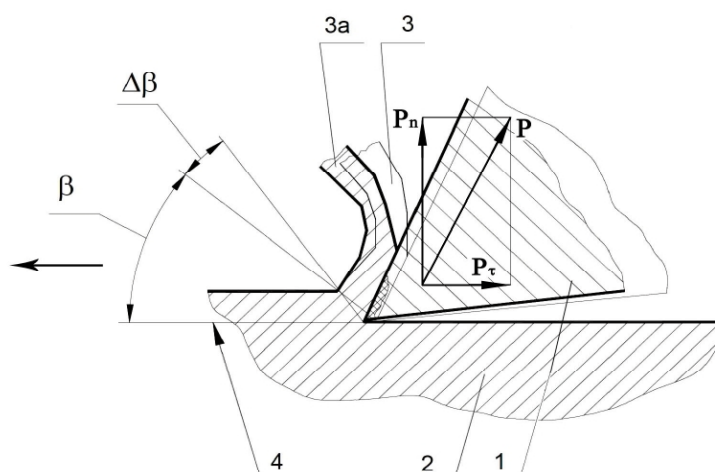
Схема действия сил на режущую кромку фрезы при высокоскоростном фрезеровании образца
